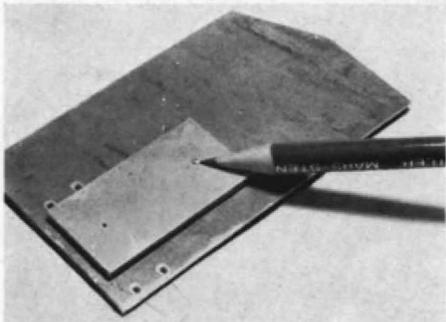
Untersicht der Weiche. Die Zungen sind aus einer als Extra-Teil eingesetzten dickeren Platte herausgefräst. Der Bleistift deutet auf den Drehpunkt dieser Platte, gegenüber liegt die Bohrung für den Stelldraht. Zur Schmierung der beweglichen Weichteile empfiehlt der Hersteller „La Beille 101“ (z. B. von Old Pullman erhältlich).
